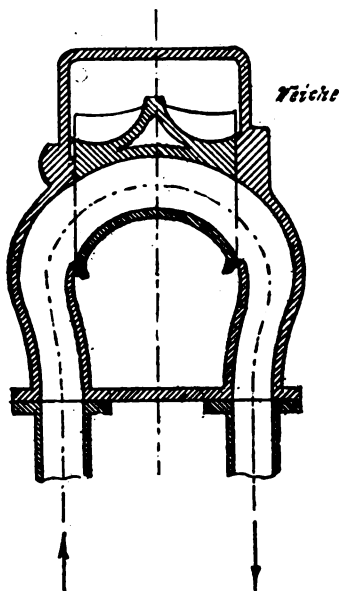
Apparat mit eingebauter Weiche auf Durchgang gestellt.
